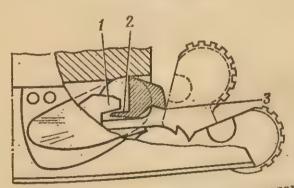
Схема блокировки курка выступом предохранителя: 7 — вуб шептала; 2 — полочка уступа предокранителя; 3 — выступ
